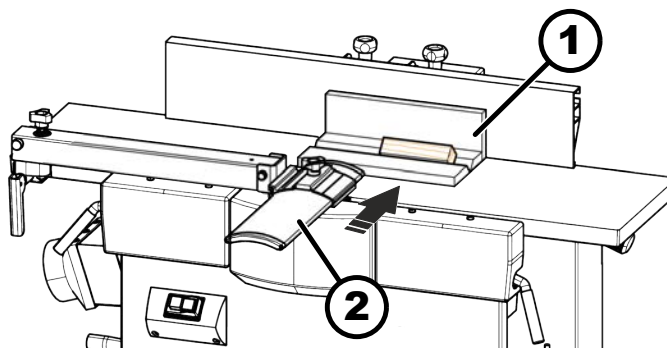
Achaflanado - Mecanizar piezas más pequeñas
